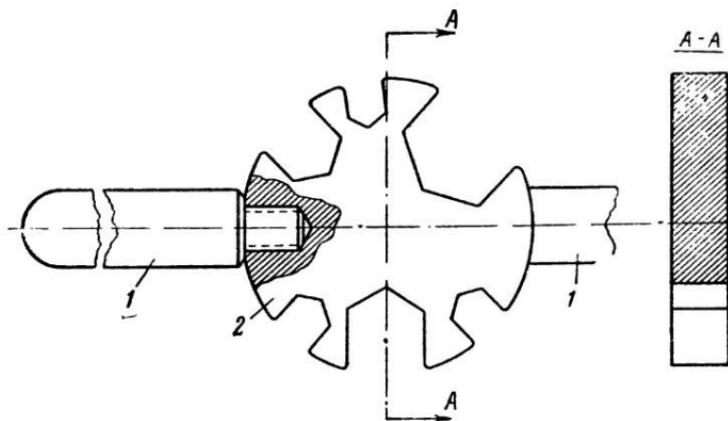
Приспособление для крепления заготовок гаек при их нарезании на сверлильном станке: 1 — упор; 2 — державка с гнездами для установки заготовок.
